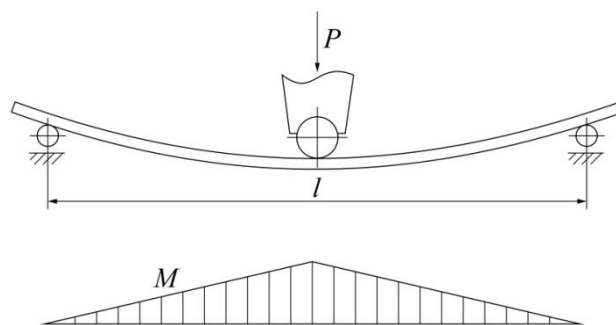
Схема изгиба заготовки силой P и эпюра изгибающих моментов
